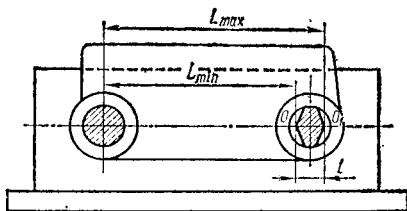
Установка детали по двум обработанным цилиндрическим отверстиям
